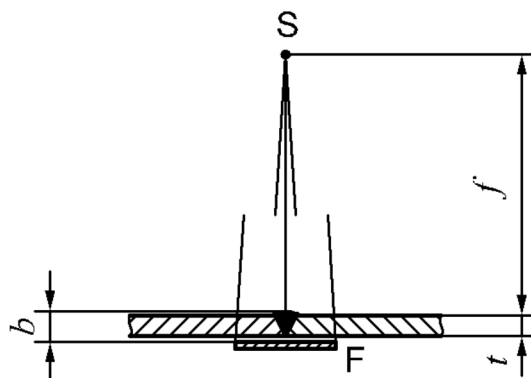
Схема контроля для плоского сварного шва при просвечивании через одну стенку
